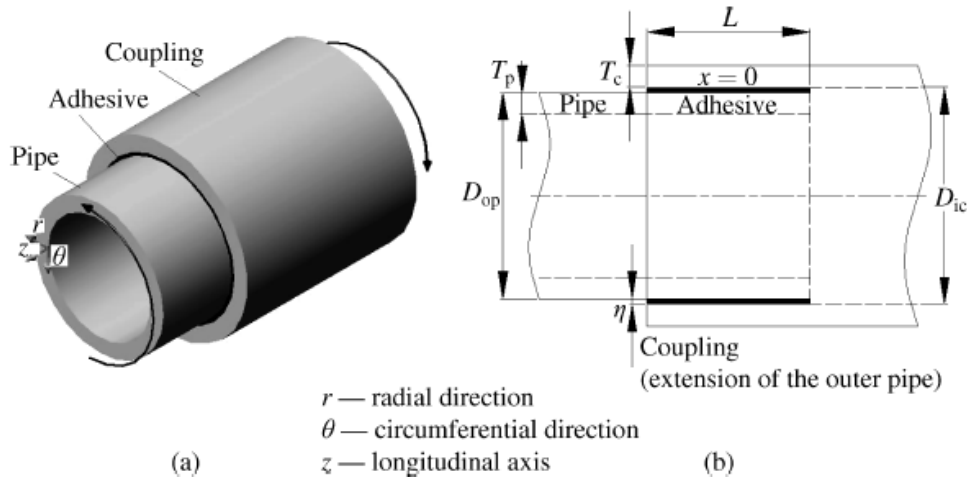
Configuração esquemática de uma junta tubular colada. (a) Constituintes conjuntos, (b) Características geométricas [28].
